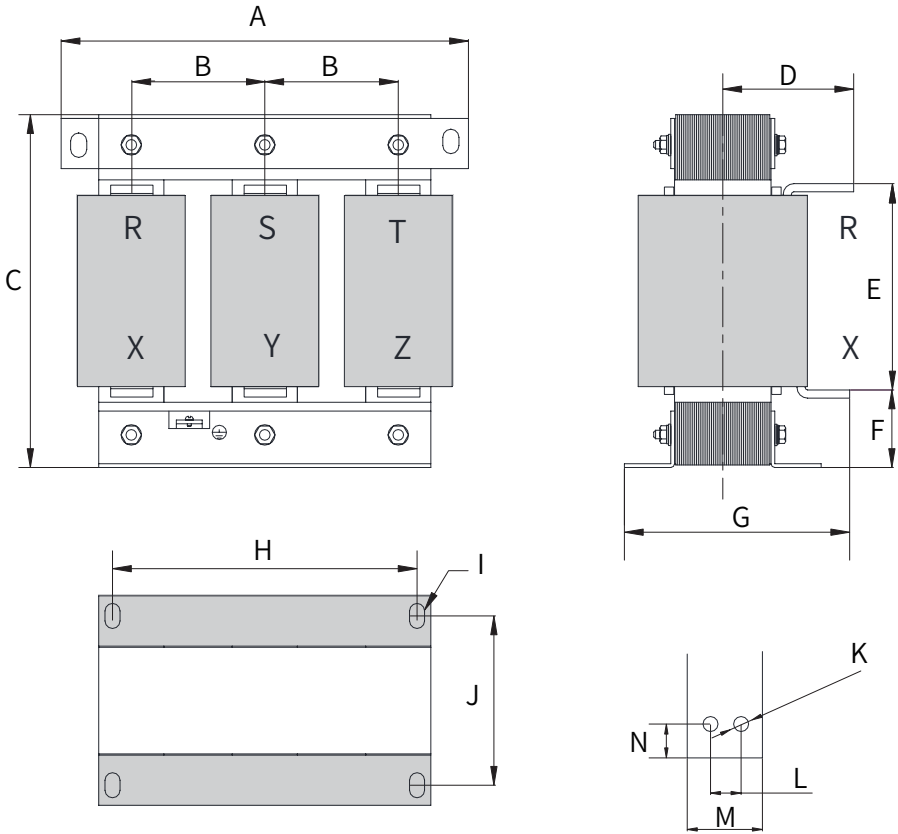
Размеры входного реактора переменного тока 490/660 А
